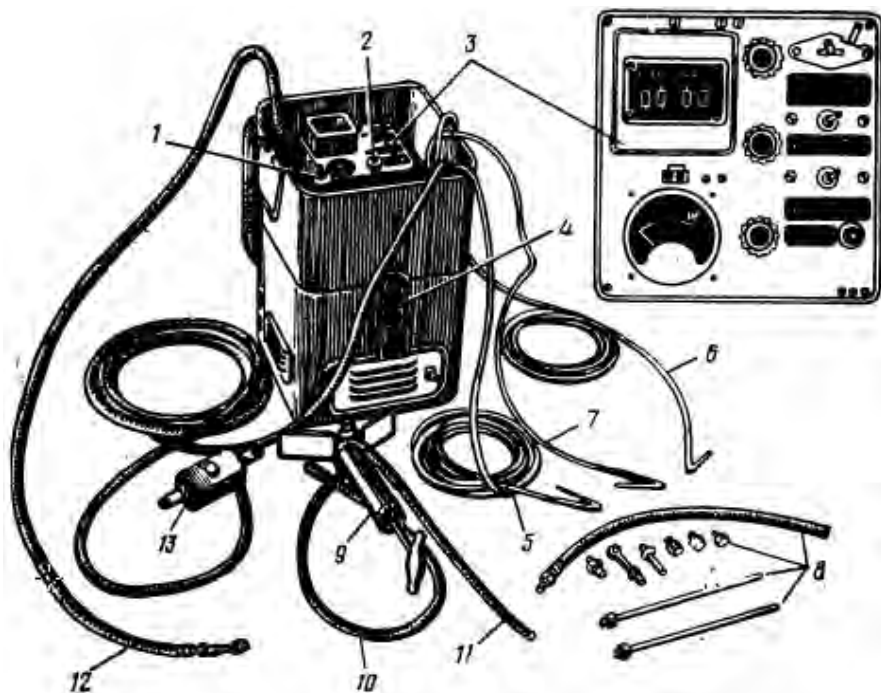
Агрегат АКД-1М для консервации двигателя и его ЗИП:
